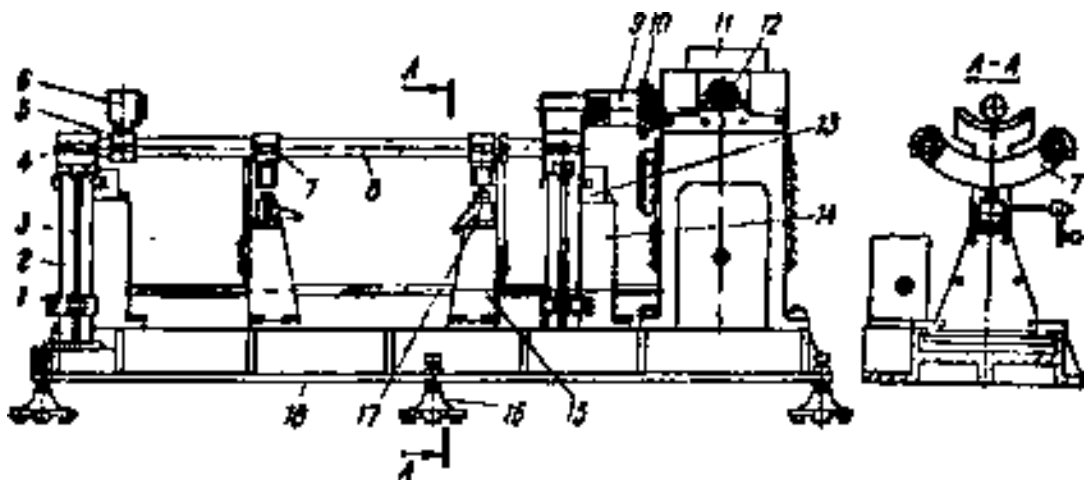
Стенд для динамічного балансування карданного валу:
